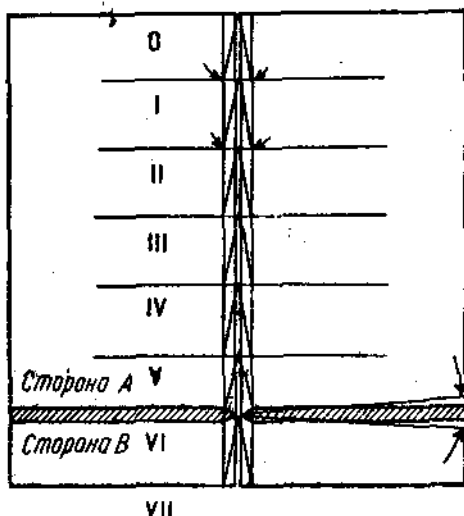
Правильный метод сварки для уменьшения явления коробления. Операция сварки ведется в таком порядке:
